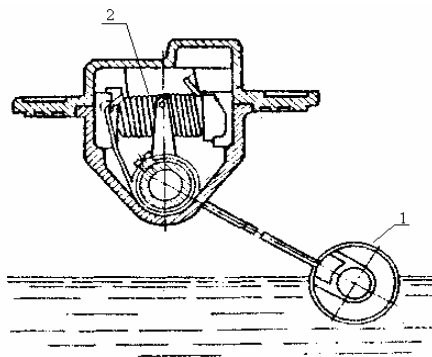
Поплавковый измерительный преобразователь: 1 – поплавок; 2 – проволочный реостат
